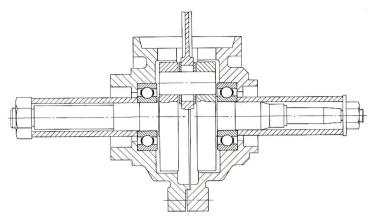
Eje cigüeñal de un pequeño motor de dos tiempos. El eje está compuesto mediante unión a presión
